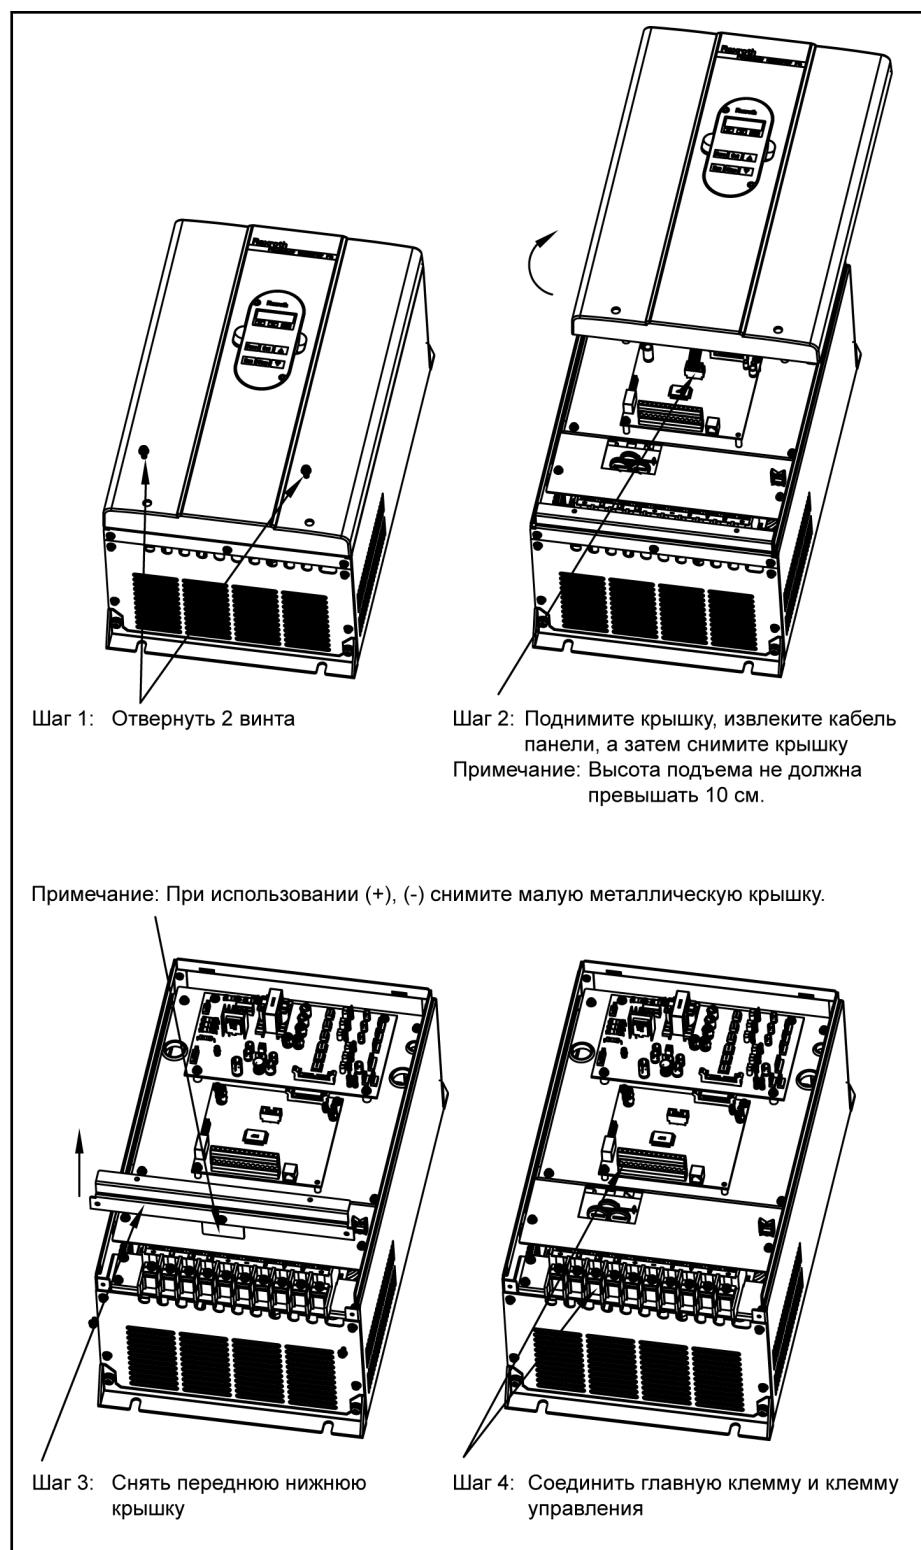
Инструкции по раскрыванию (18K5 – 37K0)
